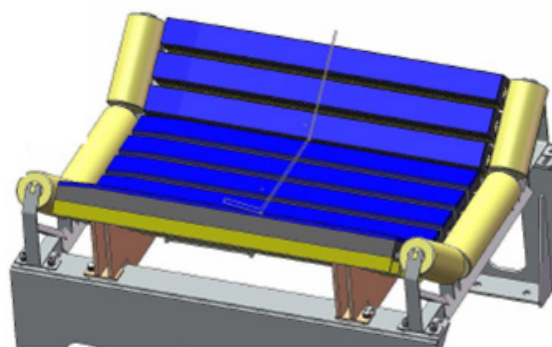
KU 300, stávající provedení dopadového místa [foto: autor]
